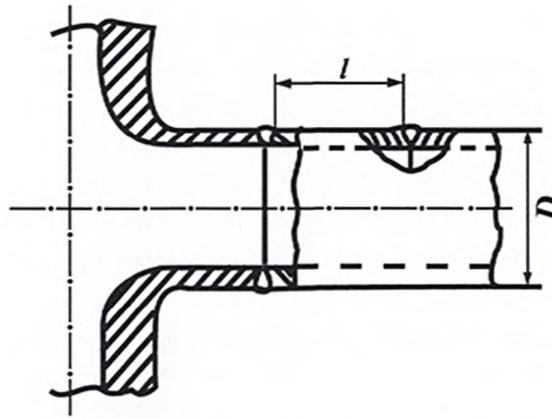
Расположение сварных соединений трубопровода с патрубком
